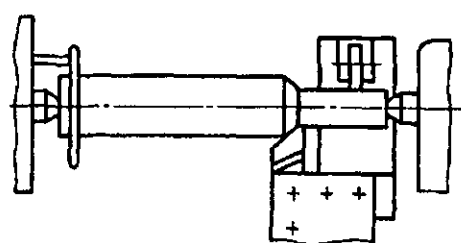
Схема установки заготовки на центрах с использованием подвижного люнета
